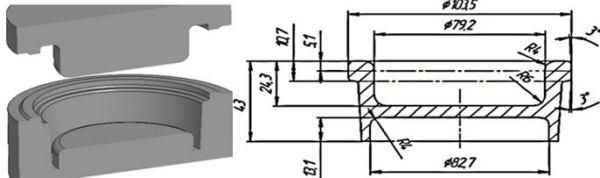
Штамп для окончательного формоизменения и готовая поковка с компенсатором в цилиндрической части поковки
